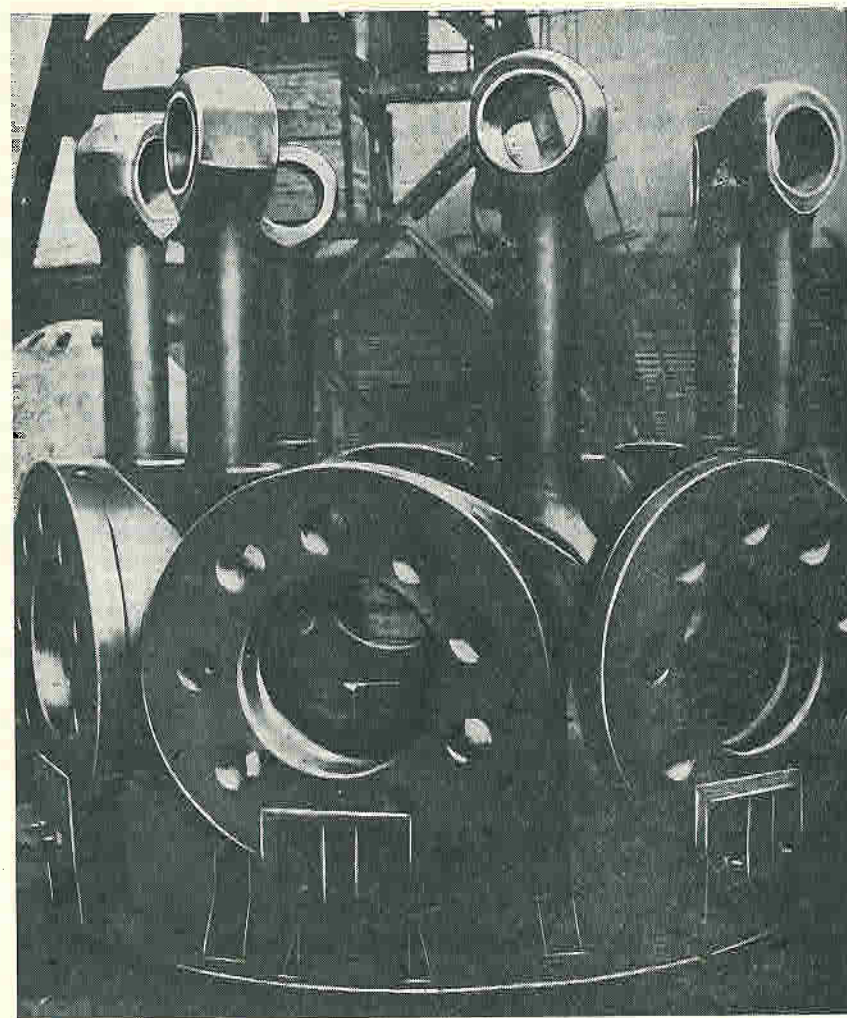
Установка рычагов с серьгами на специальном сборочном приспособлении
